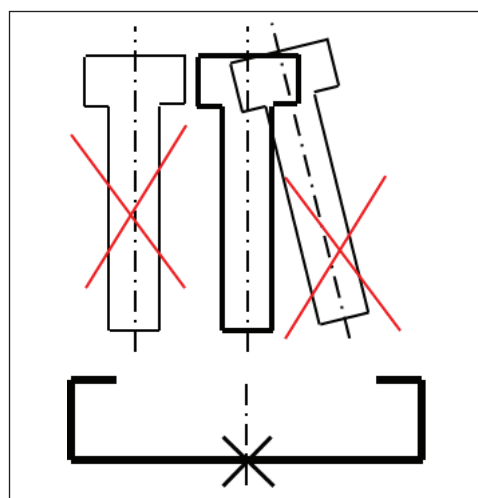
Защитная труба — важный элемент непрерывной разливки, требующий правильного позиционирования относительно металлоприемника
